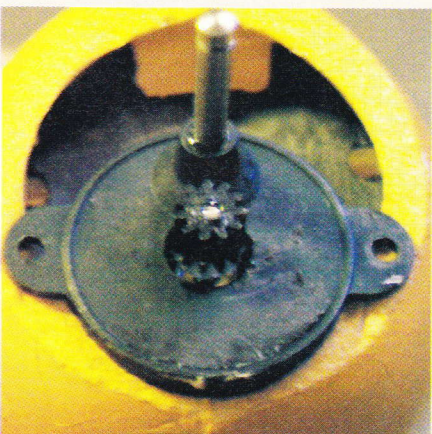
Der skal skæres i både skum og gear, før tingene kommer på plads
